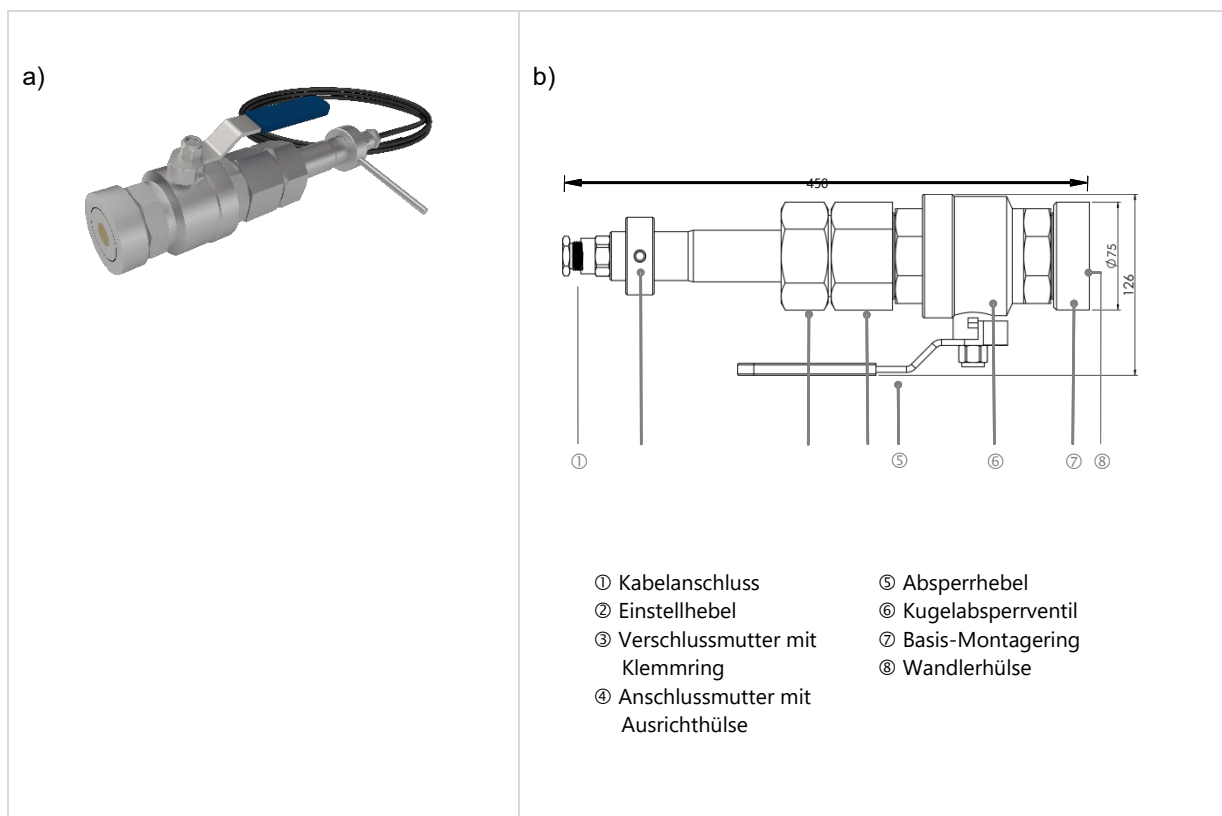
a) Einschweisssensor Übersicht, b) Abmessungen (mm)
